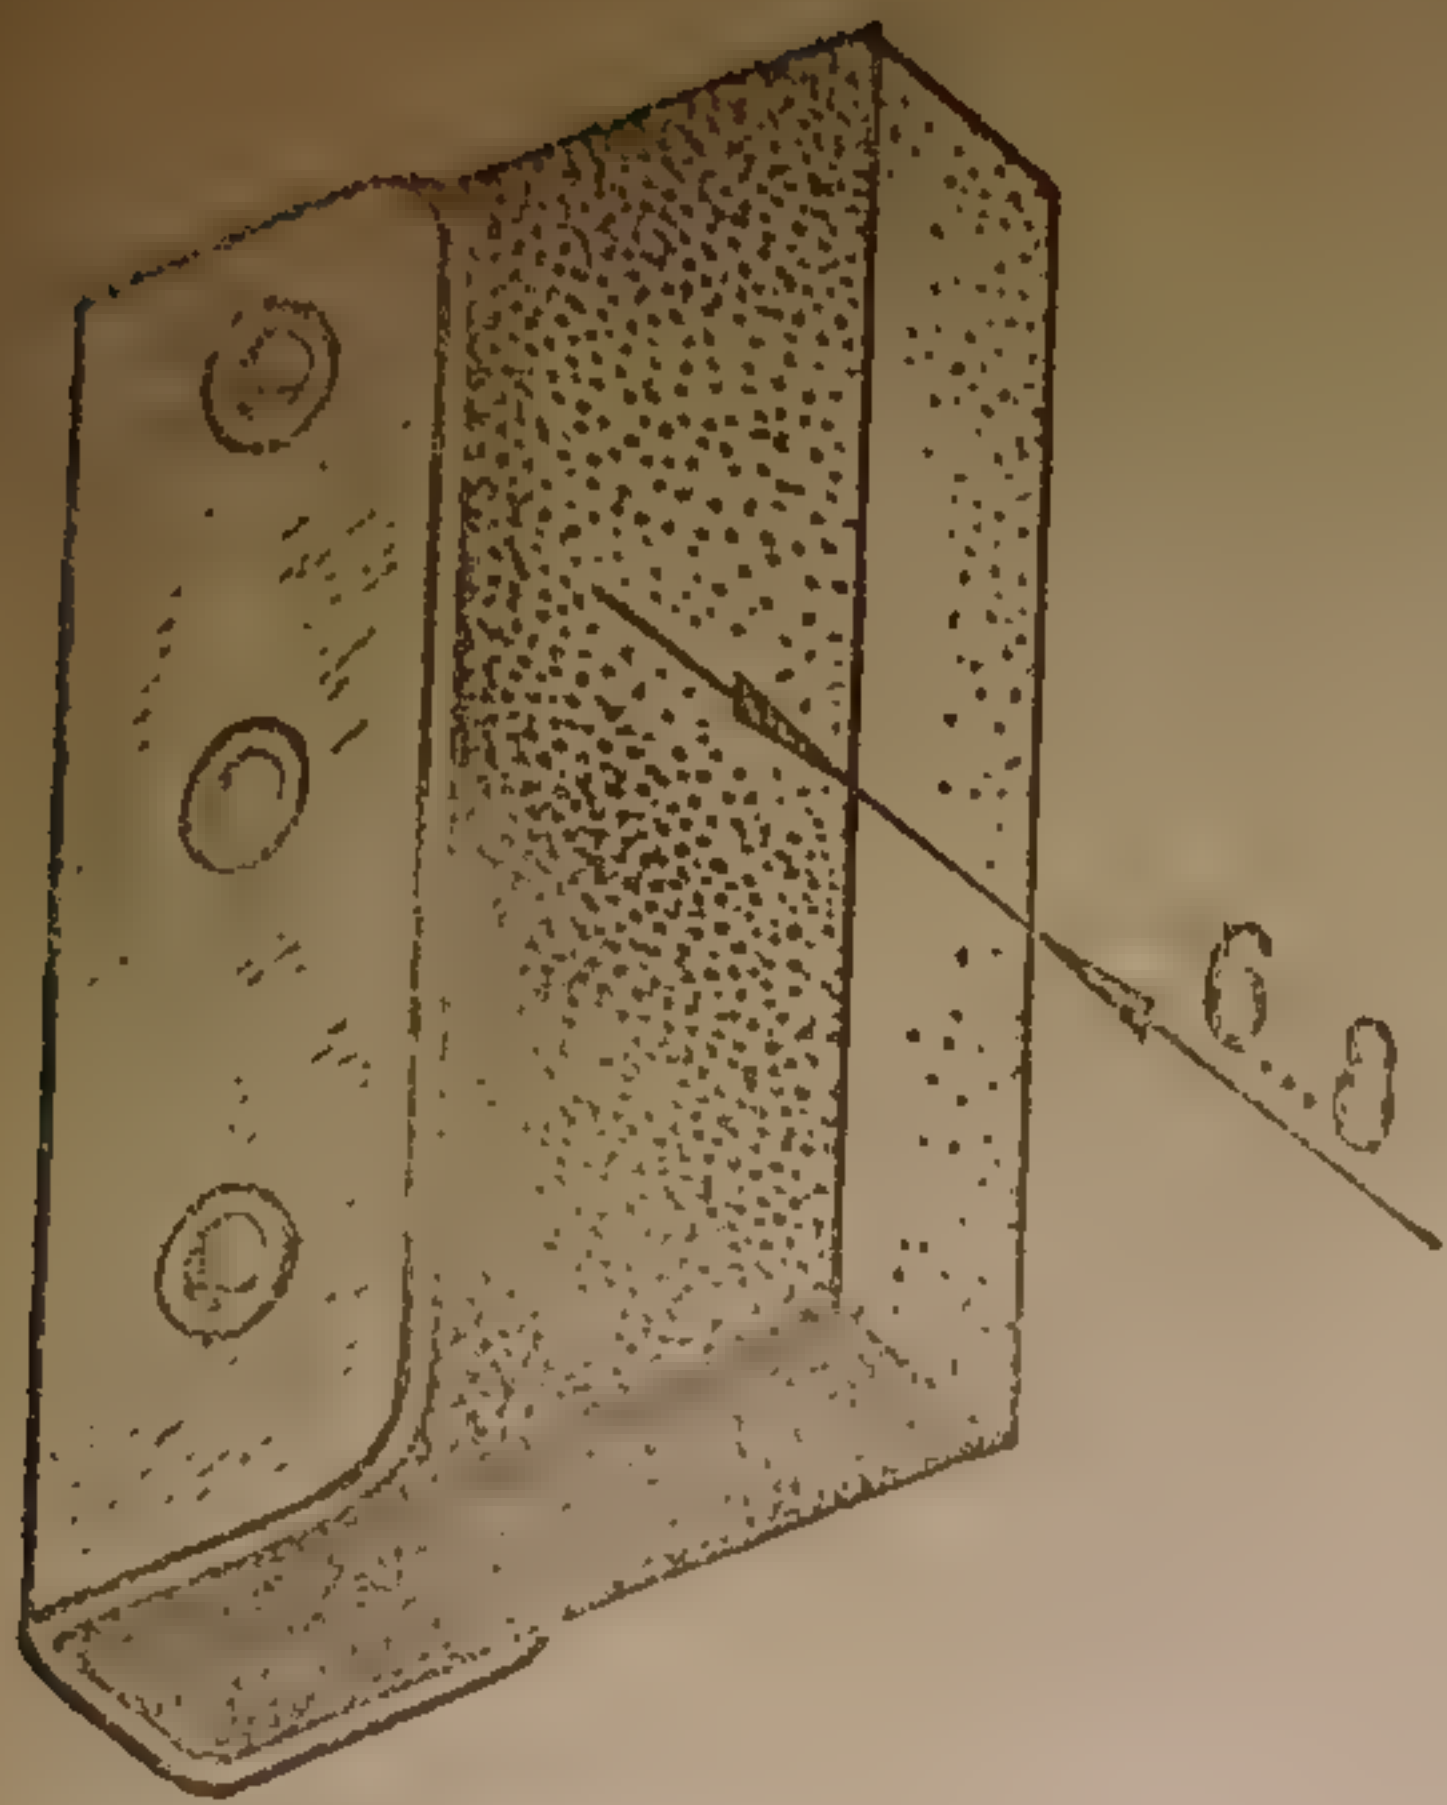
Ракель из твердой резины — основной рабочий инструмент
